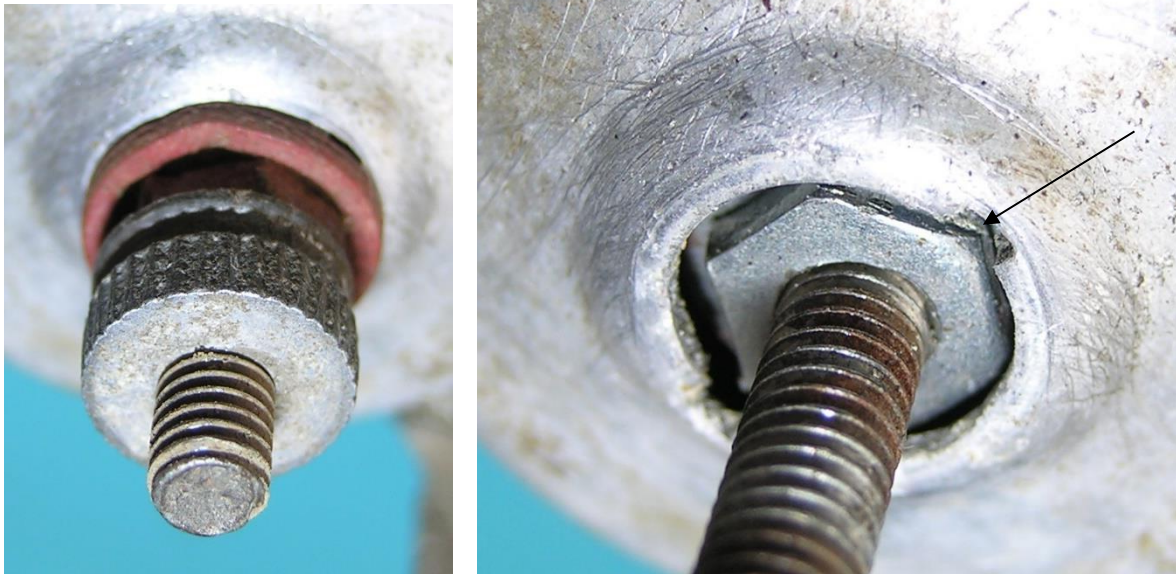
Kabelanschlussbolzen in der Bodenöffnung mit den Schlüsselnuten
